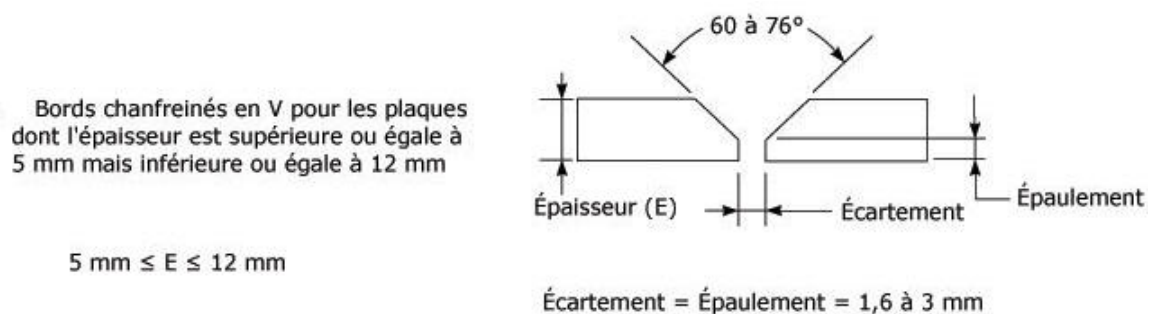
Schémas présentant la préparation des bords des pièces avant soudage.
